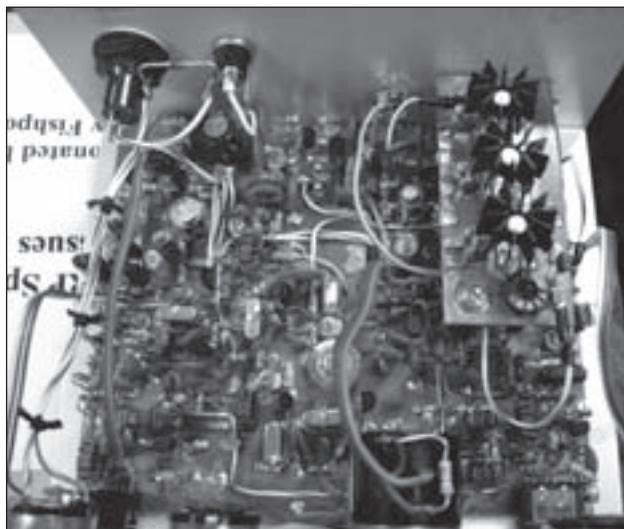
Foto A. Un transceptor de CW basado en el transistor 2N2222 montado mediante la técnica Manhattan.
